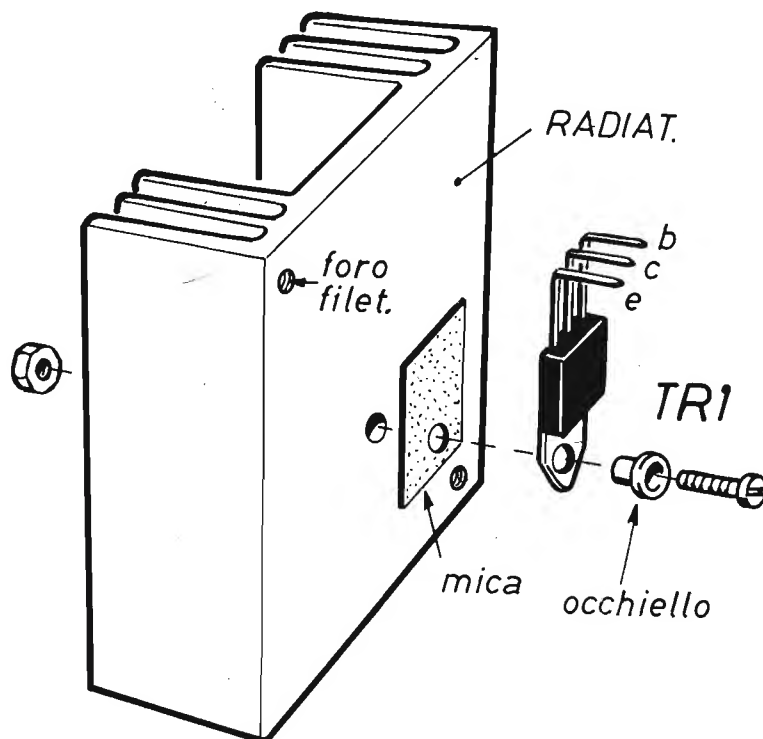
Disegno interpretativo del montaggio del transistor TR1 su dissipatore termico di elevate dimensioni.
